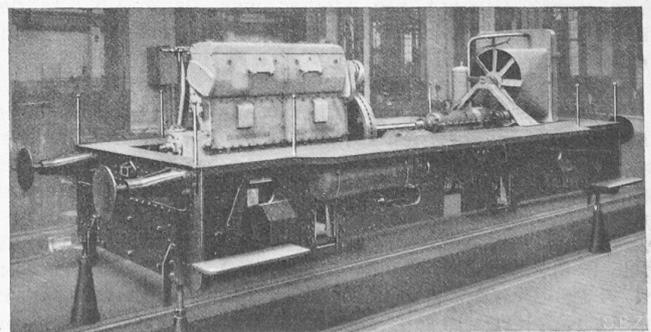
Rahmen der Lokomotive mit aufgebautem Dieselmotor und Kühler.
